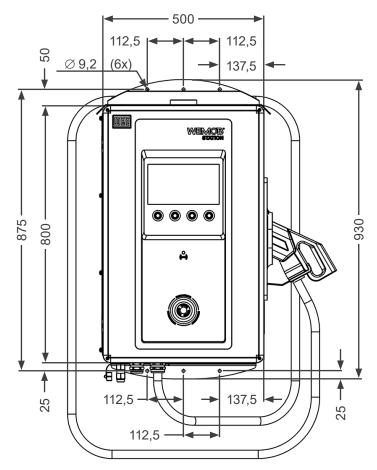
Dimensões da WEMOB-STATION (30/40 kW) - mm
